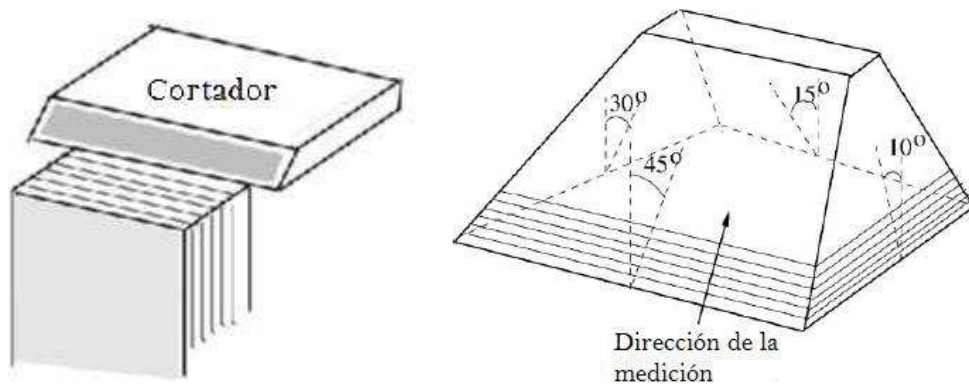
Esquema del cortador utilizado en el maquinado CNC [9].
